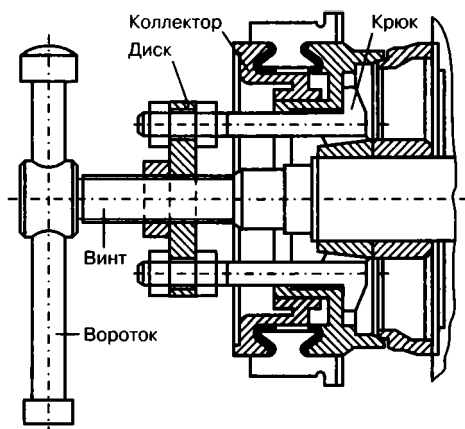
Приспособление для снятия коллектора с вала якоря
